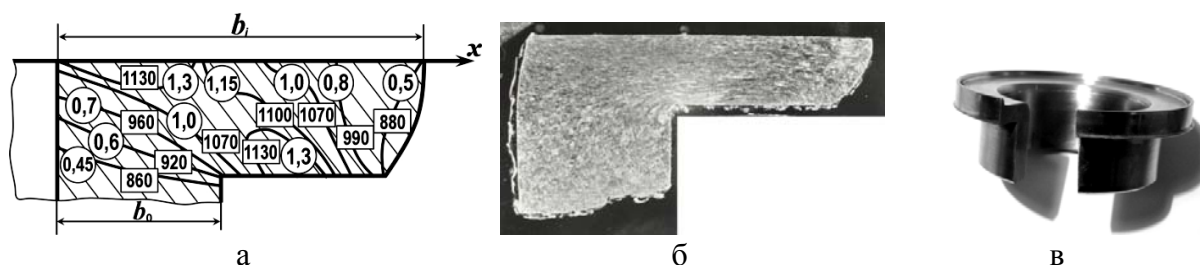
Вид сечений буртов и заготовки, полученных высадкой ХТР:
